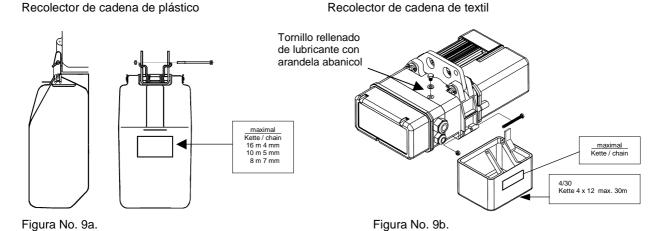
Ensamblaje del recolector de cadena y el tornillo de llenado de lubricante.
